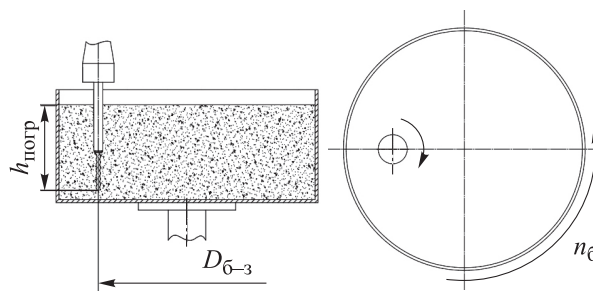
Кинематическая схема обработки заготовки потоковой галтовкой
